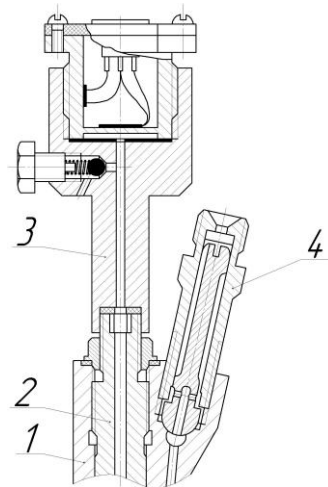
Установка датчика давления на форсунке дизеля 16ЧН 26/26: 1 – корпус форсунки; 2 – регулировочный винт; 3 – датчик давления; 4 – штуцер
